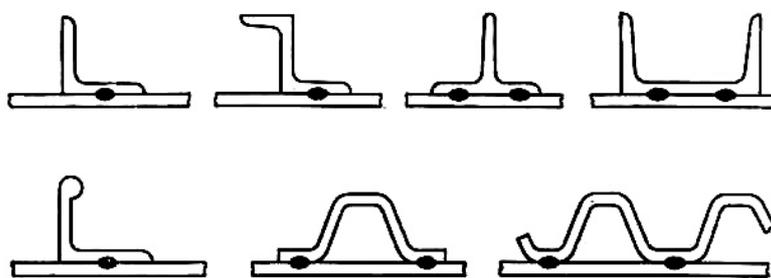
Рекомендуемые конструкции клеесварного соединения
